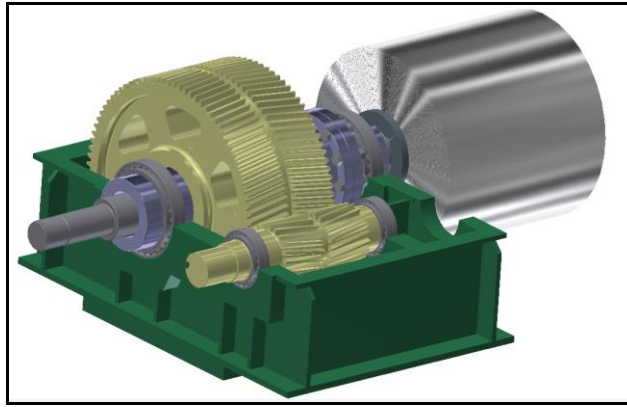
Bobinadeira do laminador Sendzimir.
